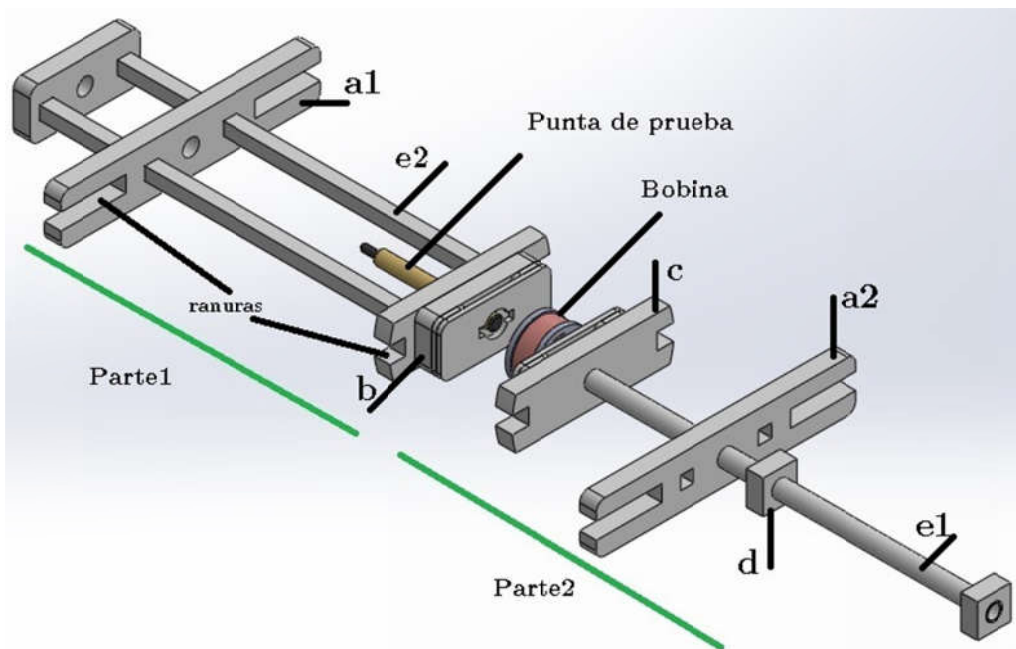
Diseño del soporte para las bobinas en SolidWorks
